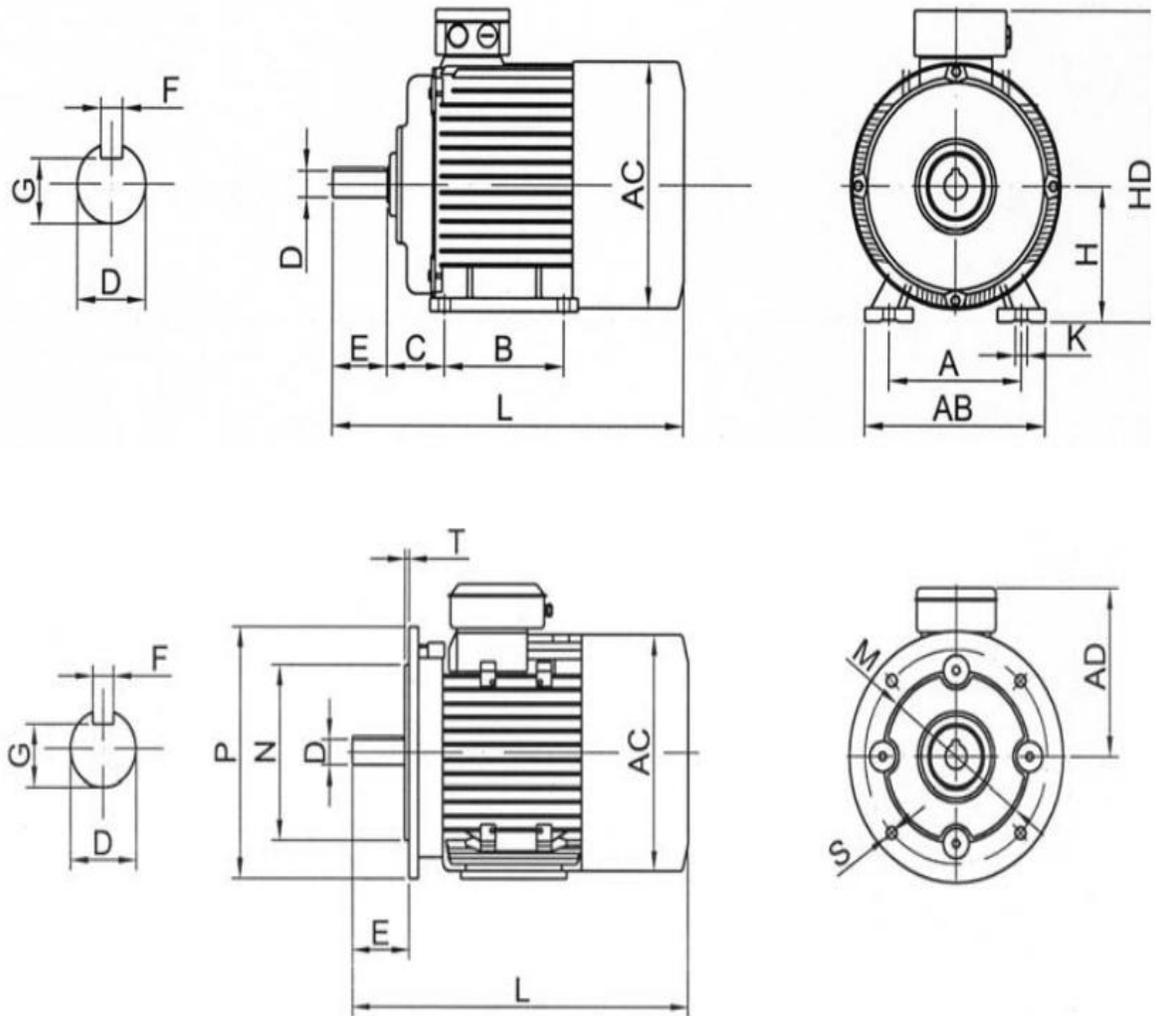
Dimensiones principales del motor trifásico asincrónico de 4 polos Kaifa MS 562-4.
